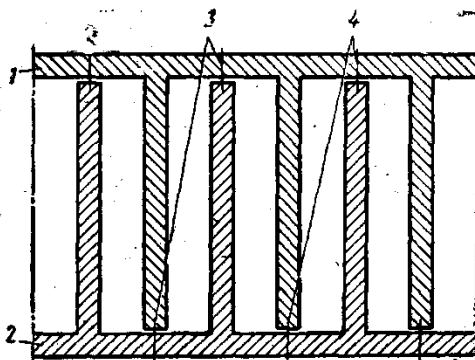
Колесо, изготовленное выфрезеровыванием:
